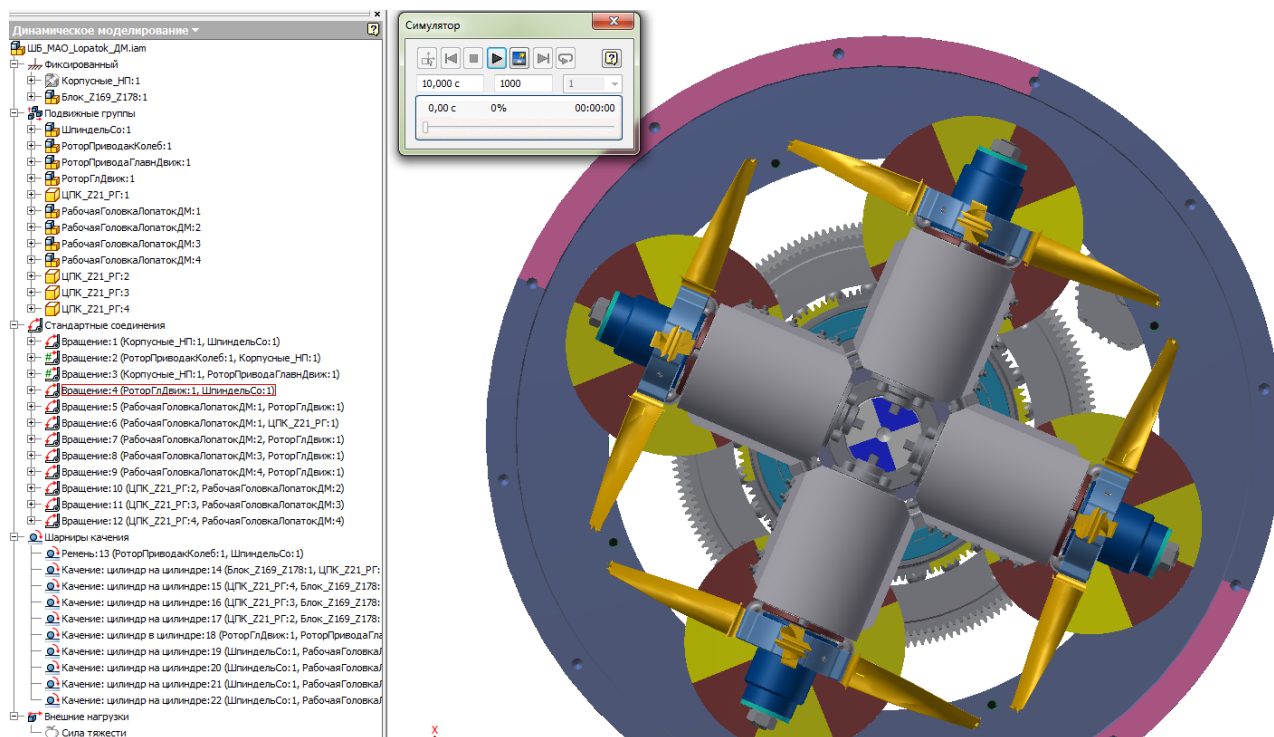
Модель роторної головки для обробки лопаток ГТД, що підготовлена для динамічного аналізу в курсах "САПР верстатів" та "Системи комп'ютерного проектування верстатів"
